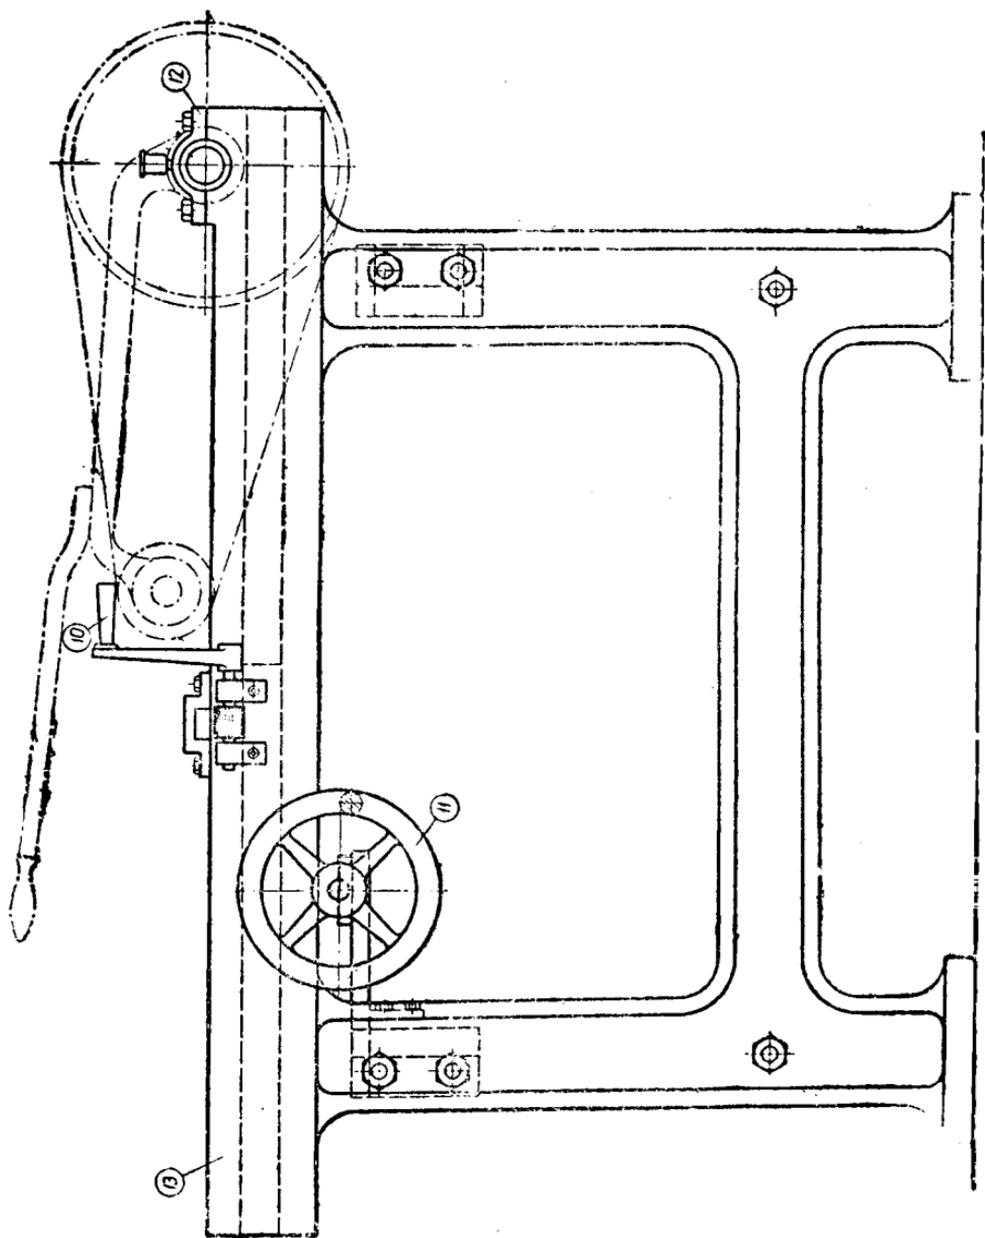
Проект станка г. Пурецкого — вид сбоку: 10 — ручка для поперечного движения приспособления с болванками; 11 — маховичок для продольного движения; 12 — подшипники для концов вала качающихся кронштейнов; 13 — место для вставки приспособления с болванками.
